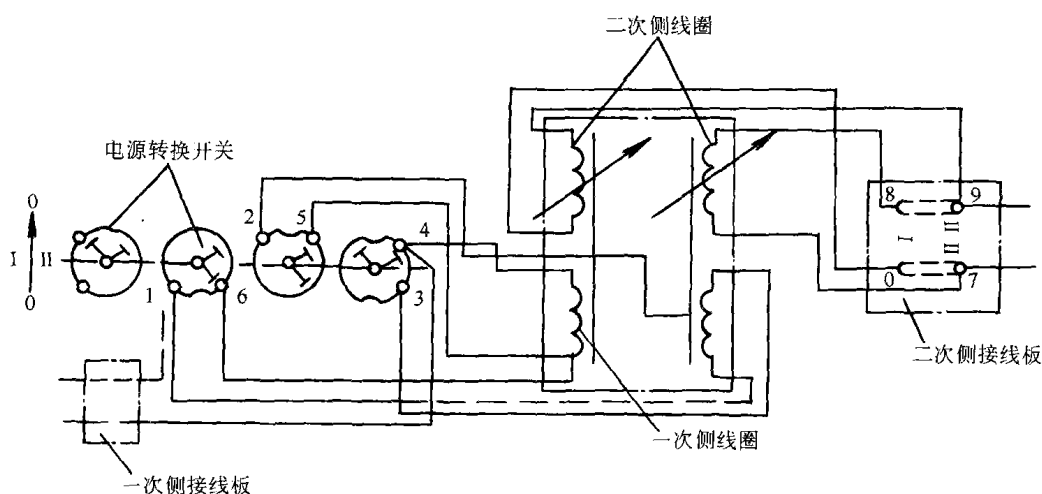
BX3—300 型弧焊变压器的结构原理图
